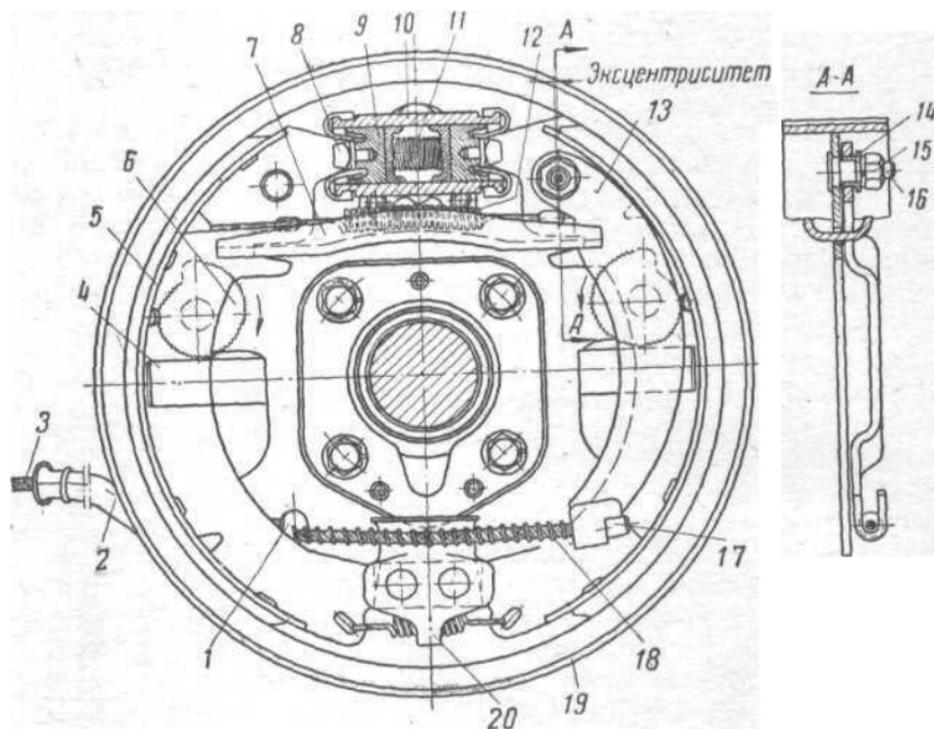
Тормозной механизм заднего колеса автомобиля модели 407: 1 — упорная шайба; 2 — направляющая трубка; 3 — трос ручного привода; 4 — прижимная пружина; 5 — тормозная колодка; 6 — регулировочный эксцентрик; 7 — распорная планка; 8 — сухарь поршня; 9 — поршень колесного цилиндра; 10 — колесный цилиндр; 11 — пружина; 12 — стяжная пружина; 13 — разжимной рычаг; 14 — втулка регулировочного «инта»; 15 — гайка; 16 — регулировочный винт; 17 — наконечник троса; 18 — пружина троса; 19 — опорный тормозной диск; 20 — накладка опорной пластины
